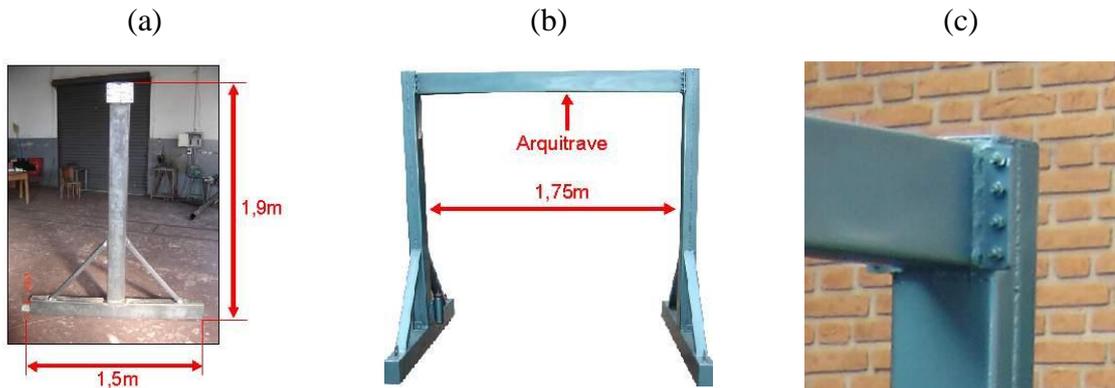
Estrutura metálica tipo "T" Invertido (a), Arquitrave (b) e União Parafusada (c)
